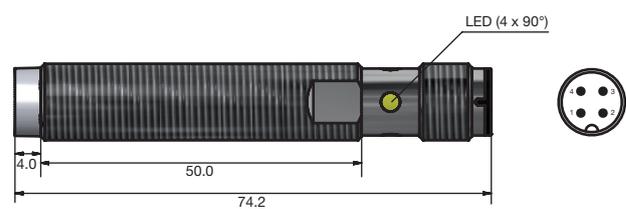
Lange Ausführung, Nicht bündiger Einbau, Steckversion
